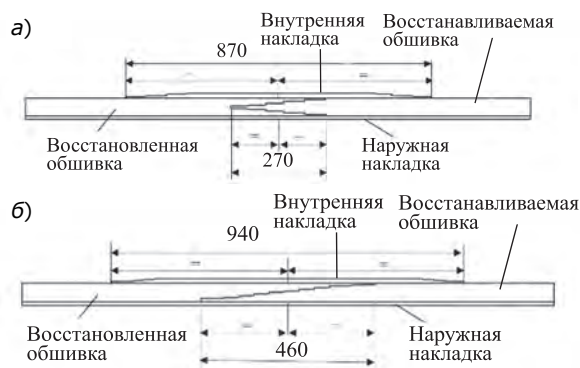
Узел стыкового соединения частей обшивки корпуса: а) с симметричной ступенчатой разделкой кромок; б) с несимметричной ступенчатой разделкой кромок
